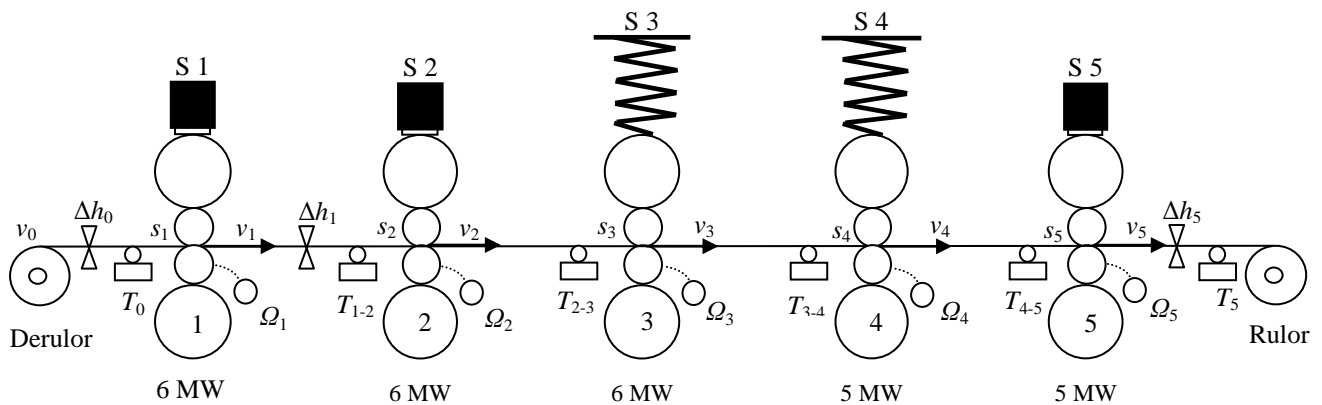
Principalele utilaje din cadrul unui laminor tandem convențional
